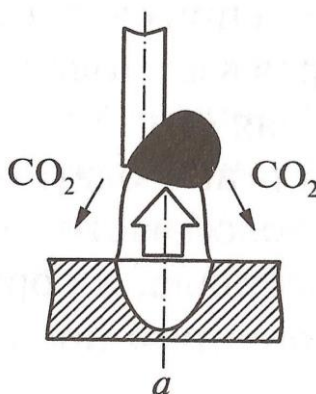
Формирование капли электродного металла при сварке в CO_2
